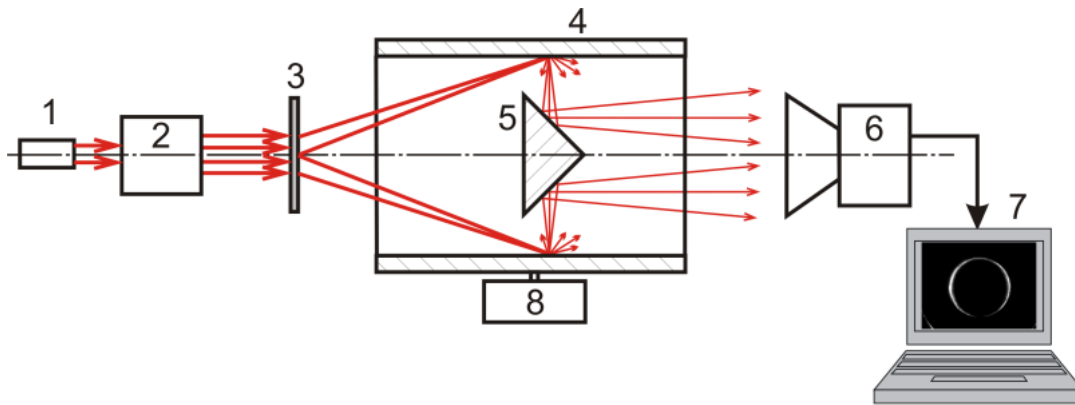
Принцип контроля отверстий: 1 – лазер; 2 – коллиматор; 3 – ДОЭ; 4 – цилиндрический канал; 5 – коническое зеркало; 6 – камера; 7 – компьютер; 8 – устройство перемещения детали
